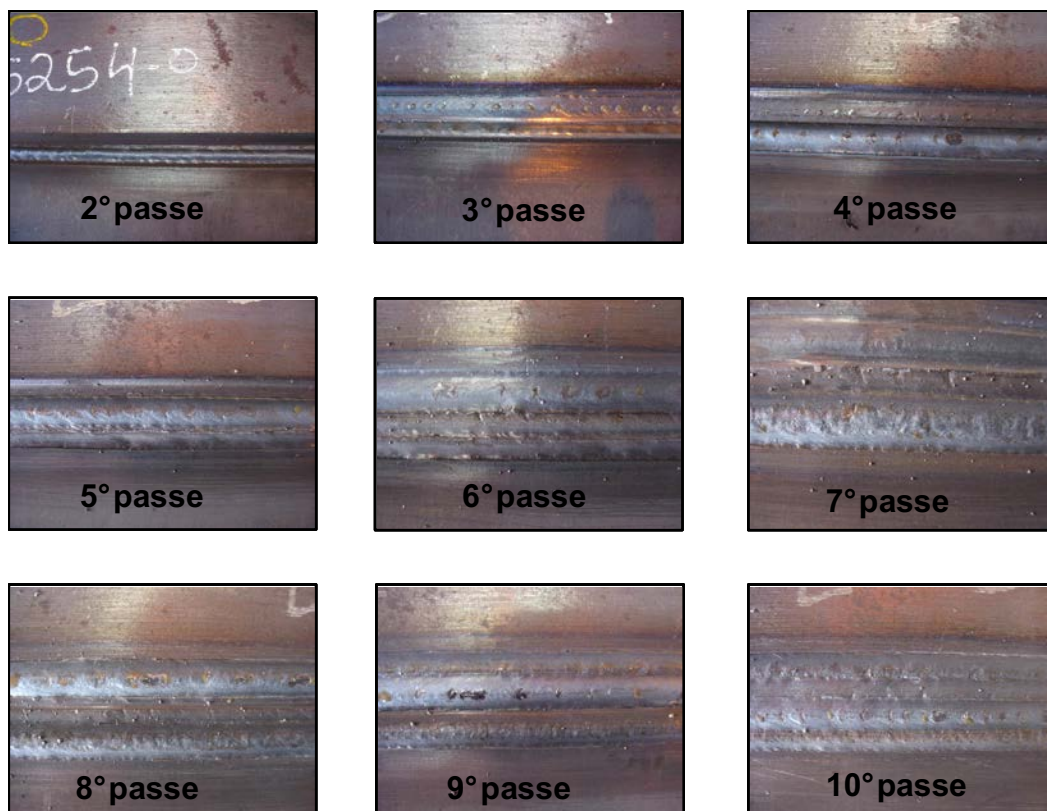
Corpo de prova após a execução dos passes de soldagem de 2 a 10.
